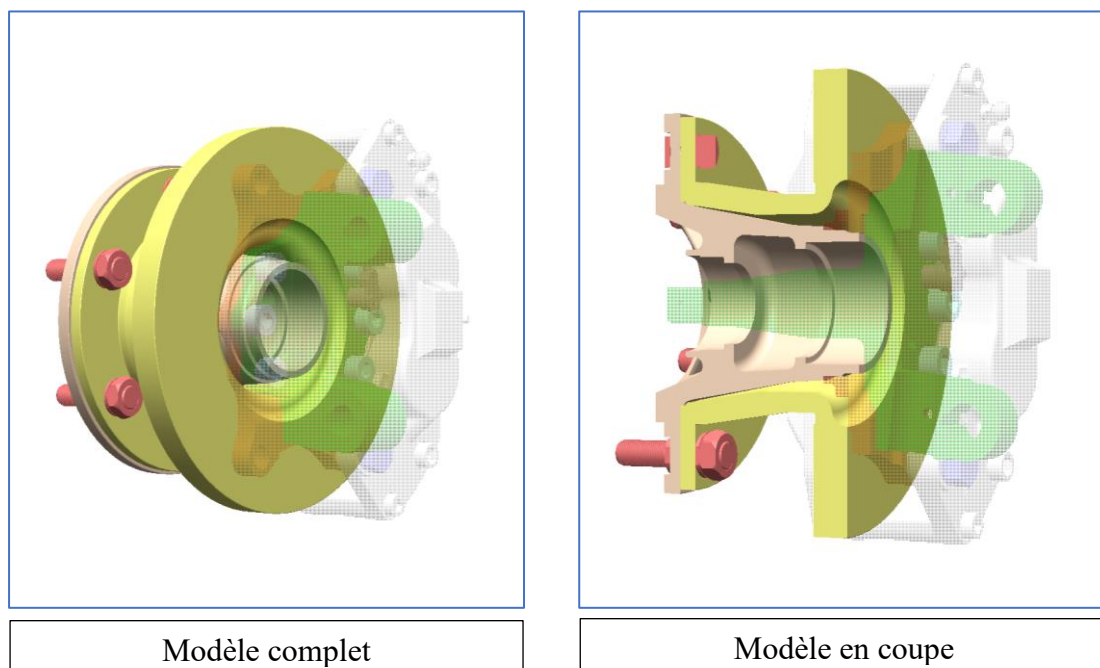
Sous-ensemble Disque-Moyeu-Goujon dessiné avec SolidWorks
